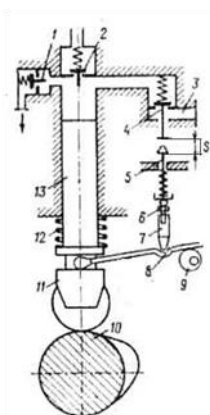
ТНВД клапанного типа с регулировкой по концу подачи: 1 — предохранительный; 2 - нагнетательный клапаны; 3 - магистраль; 4 - перепускной (всасывающий) клапан; 5 - составной толкатель; 6 - регулировочный болт; 7 - толкатель; 8 - рычаг; 9 - эксцентриковый валик; 10 - кулачная шайба; 11 - ролик толкателя; 12 - возвратная пружина; 13 - плунжер; S - зазор
